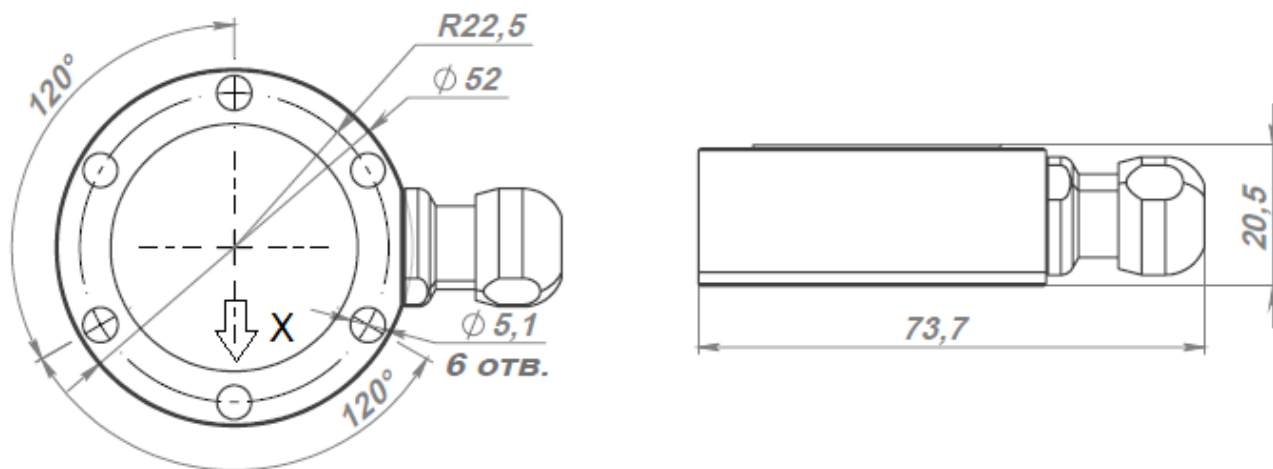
Габаритные и присоединительные размеры измерителя IN-Q2M
